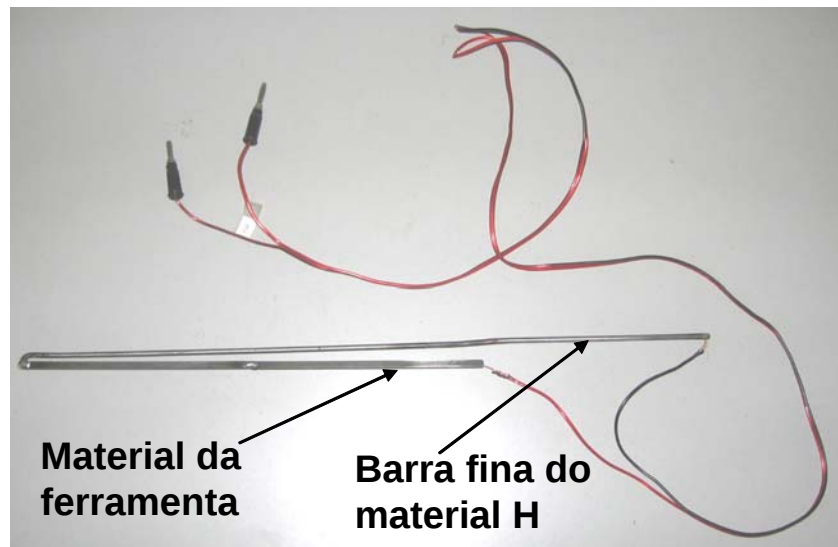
Junta soldada do termopar ferramenta-peça para calibração do sistema
